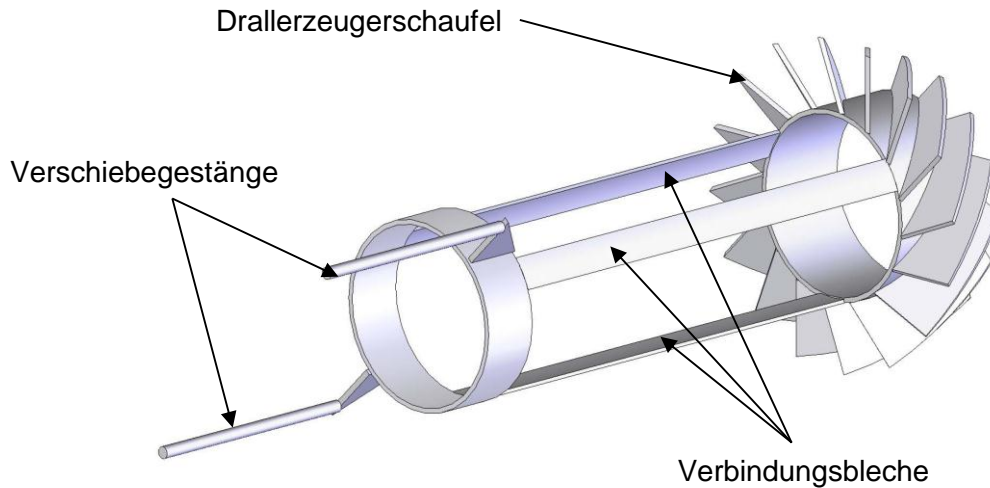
Prinzipskizze des Drallerzeugers
